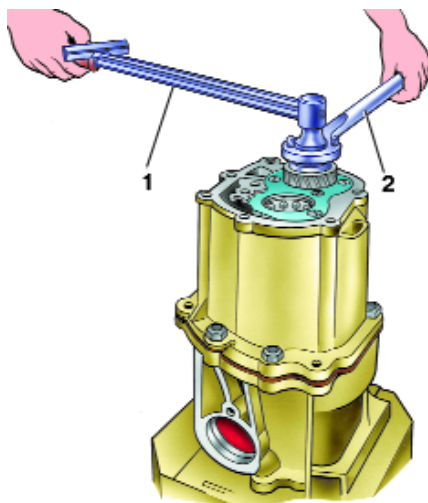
Затяжка гайки ведущей шестерни при определении монтажного размера С: 1 – динамометрический ключ; 2 – специальный ключ для стопорения шестерни
